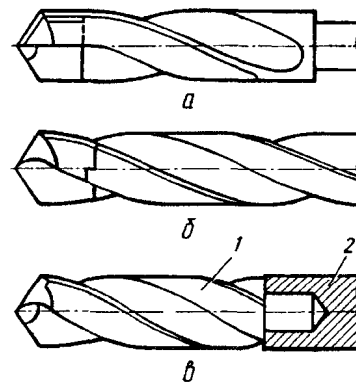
Твердосплавні свердла: а - з упаяною пластинкою; б - з припаяною коронкою; в - суцільне твердосплавне: 1 - робоча частина, 2 - хвостовик
